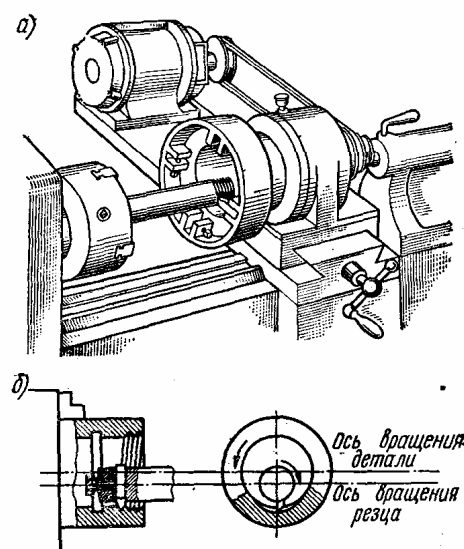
Нарезание резьбы вращающимися резцами: а – головка для четырех резцов (в положении, показанном на рисунке, установлен только один резец); б – схема нарезания внутренней резьбы
